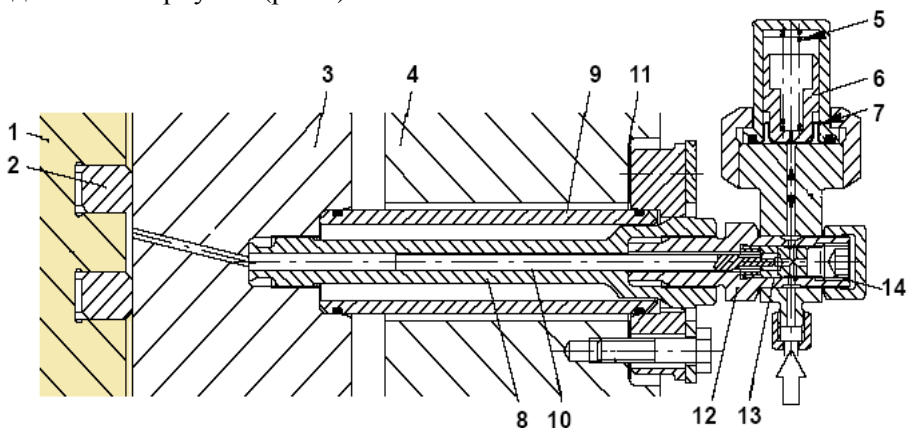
Составляющие 2-х рядной лубрикаторной системы двигателей RTA: 1-поршень двигателя; 2-поршневое кольцо; 3-цилиндрическая втулка; 4-рубашка; 5-пружина; 6-поршень аккумулятора; 7- мембрана; 8-корпус шту-
